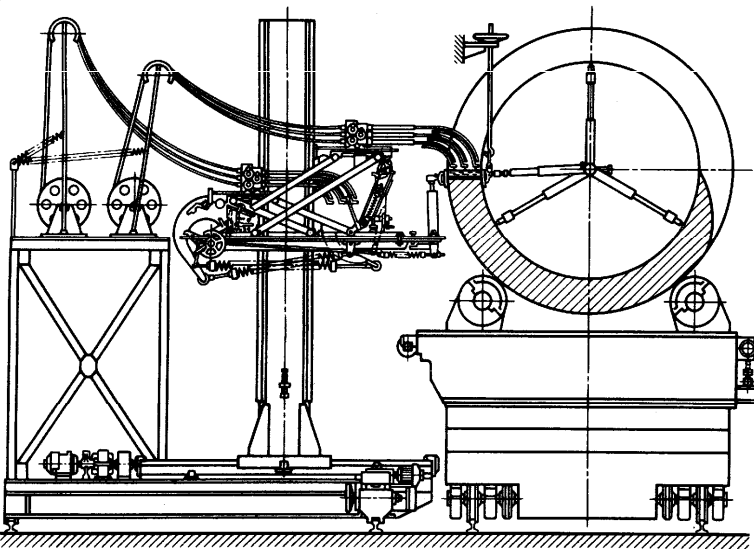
Дубль-аппарат для электрошлаковой сварки и устройство внутреннего ползуна
